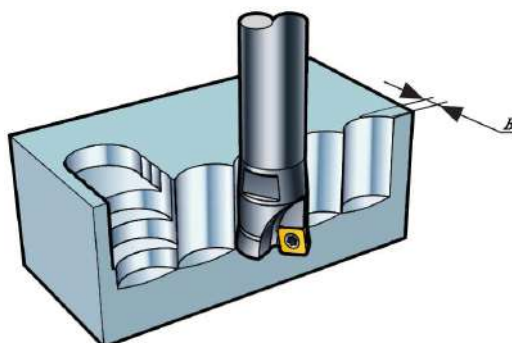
Ширина фрезерування при плунжерному фрезеруванні [5]
